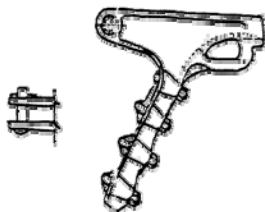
Mordaza de Amarre Tipo Pistola. *Bolted Type dead end Clamp
